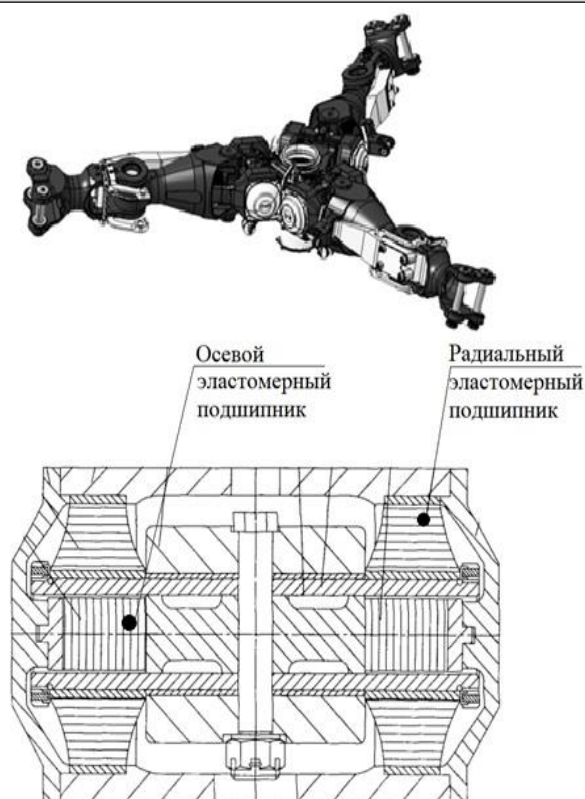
Трехшарнирная втулка с эластомерными подшипниками в шарнирах
